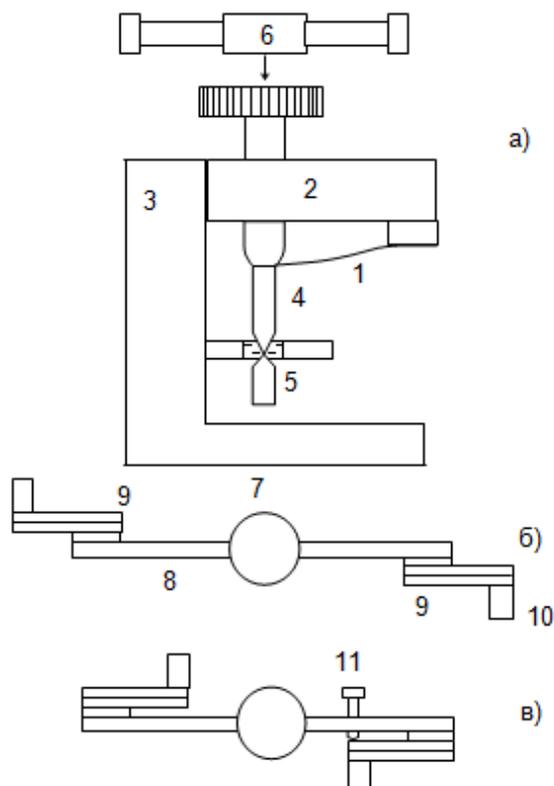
Устройство перемещения заготовки СТМ-зонда: а – схема; б, в – конструкция актюатора
